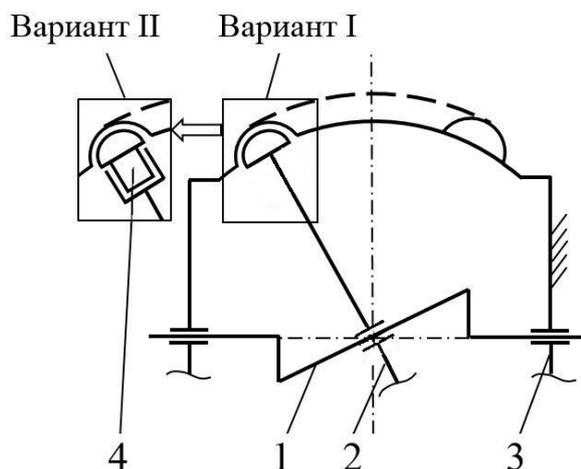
Кинематическая схема двухзвенной роликовой передачи: 1 – ведущий вал с эксцентриком; 2 – генератор; 3 – корпус с беговой дорожкой; 4 – ролик
